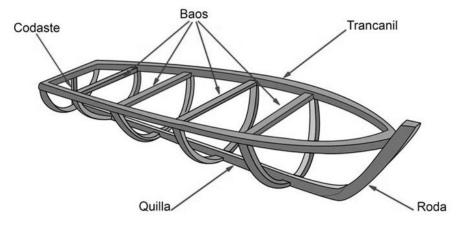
SAILANDTRIP (2014). Esquema de la estructura básica.de un barco.
